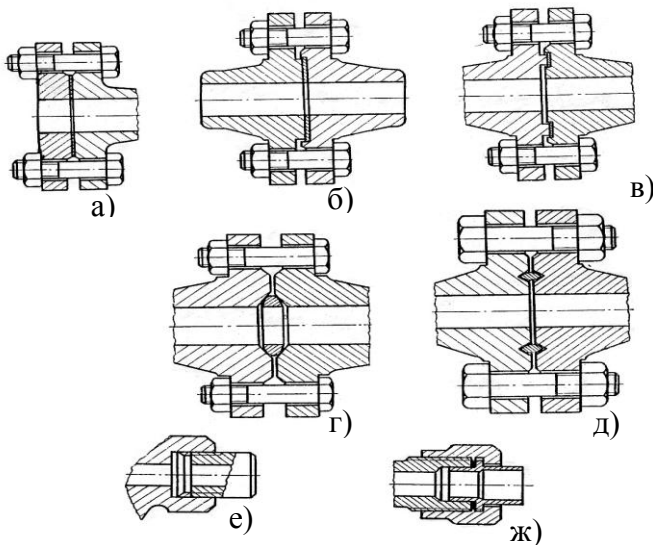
Основные типы присоединения арматуры к трубопроводу:
